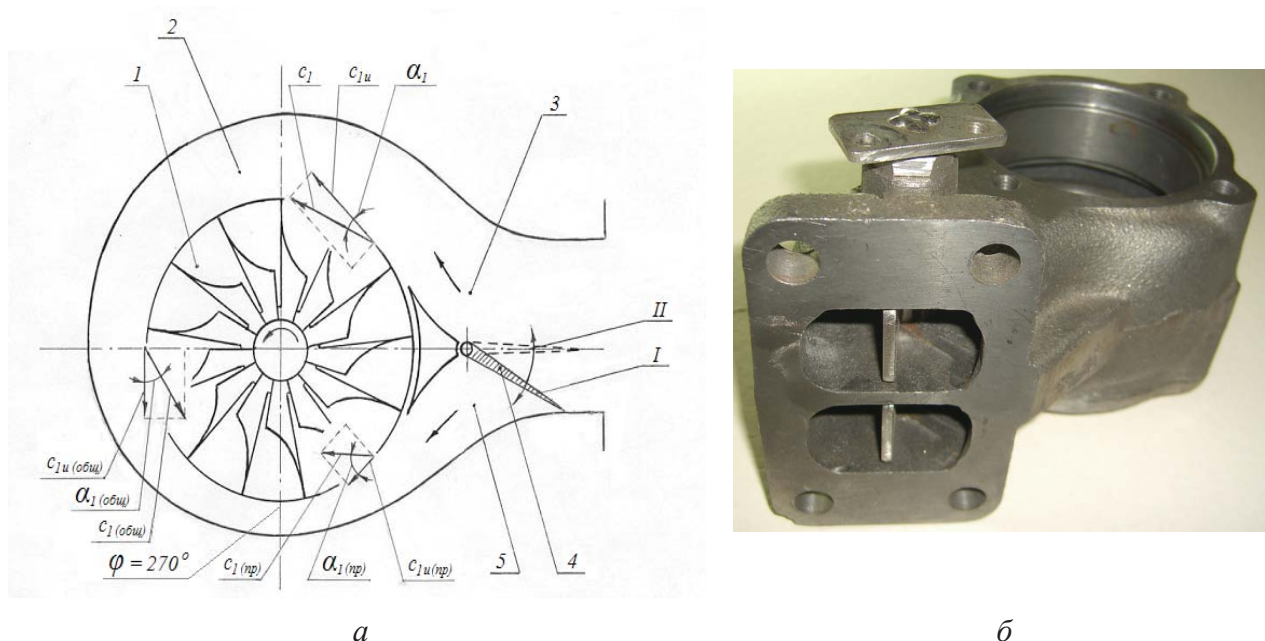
Схема способа регулирования (а) и корпус турбины (б)
